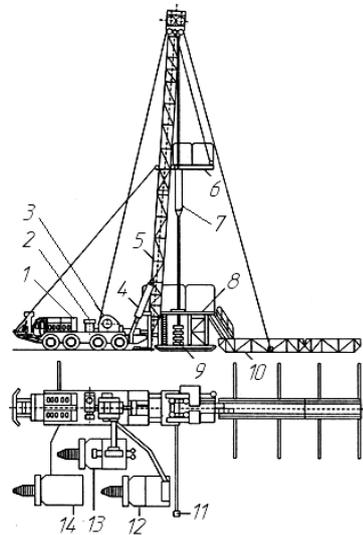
Установа для ремонту і освоєння свердловин КОРО 1-80:
